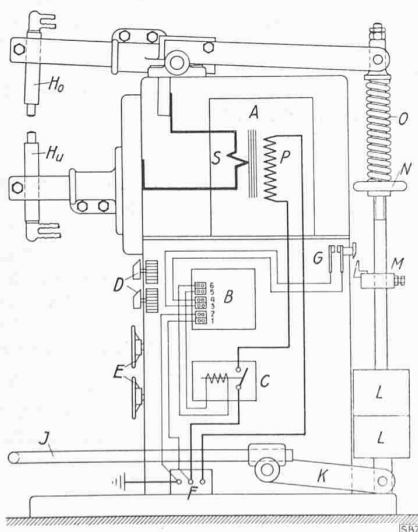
Schaltschema der Punktschweißmaschine, Modell GPS der A. G. Schlatter, Zollikon
